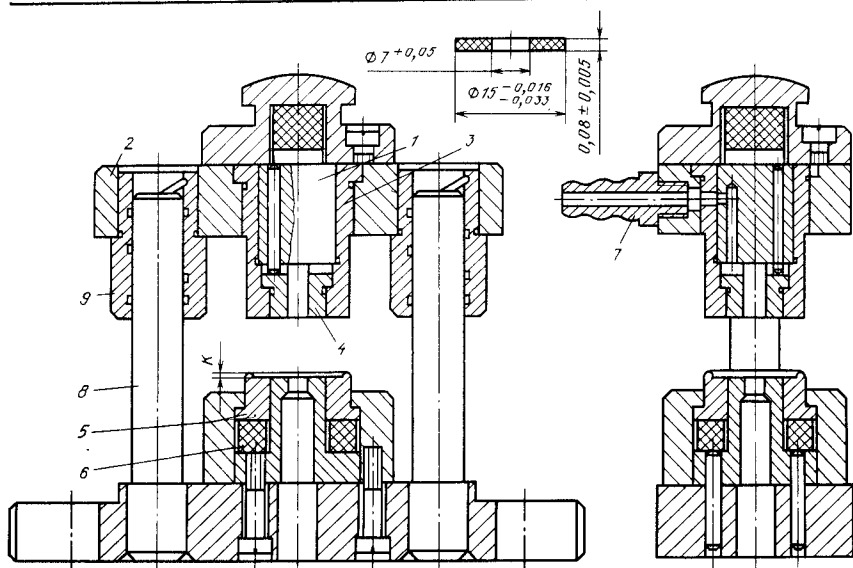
Конструкция совмещенного штампа для вырубki—пробивки деталей из слюды
